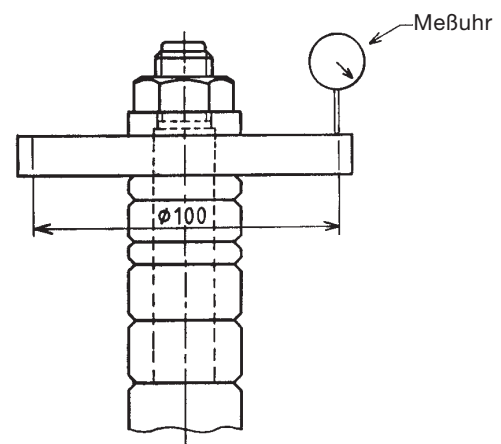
Prüfanordnung für den Planlauf-Test von Spindelring-Sätzen
